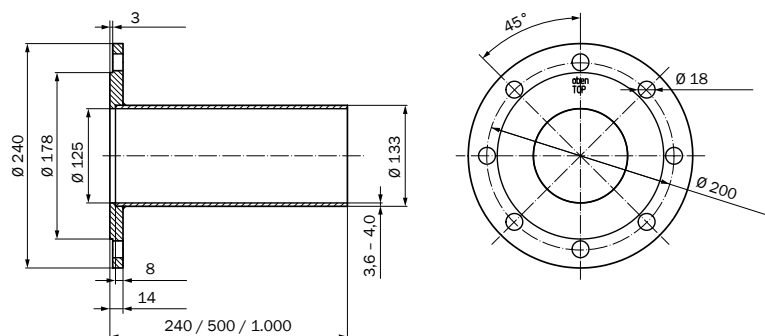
Montageflansch DN100 (alle Angaben in mm)
